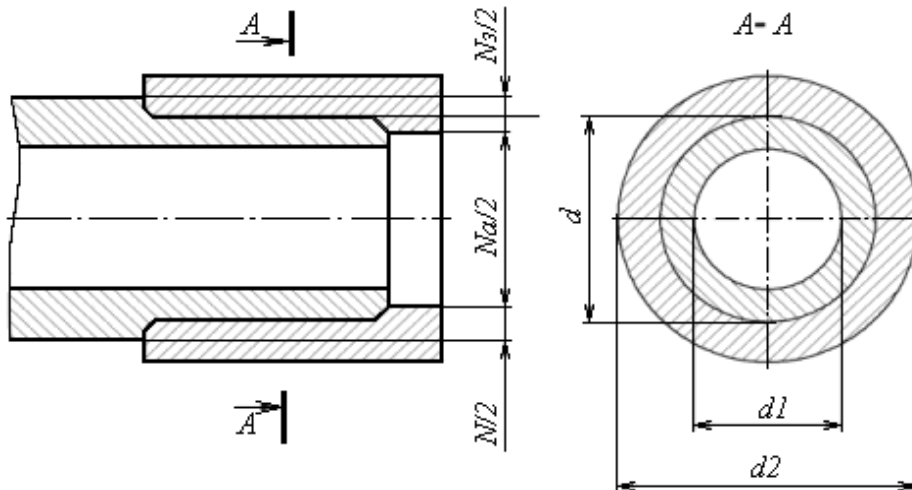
Схема з'єднання втулки з валом при посадці з натягом
